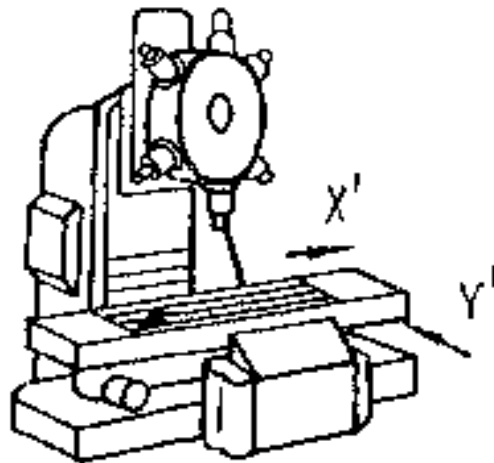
Компонувальна схема вертикально-фрезерного верстата з револьверною головкою.
